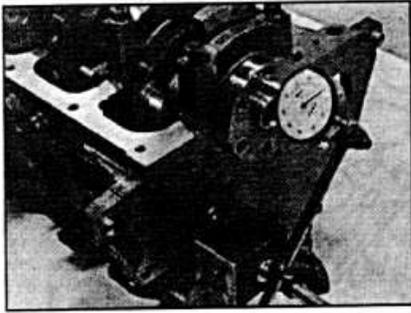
D.56. Проверка осевого люфта коленчатого вала индикатором часового типа.
